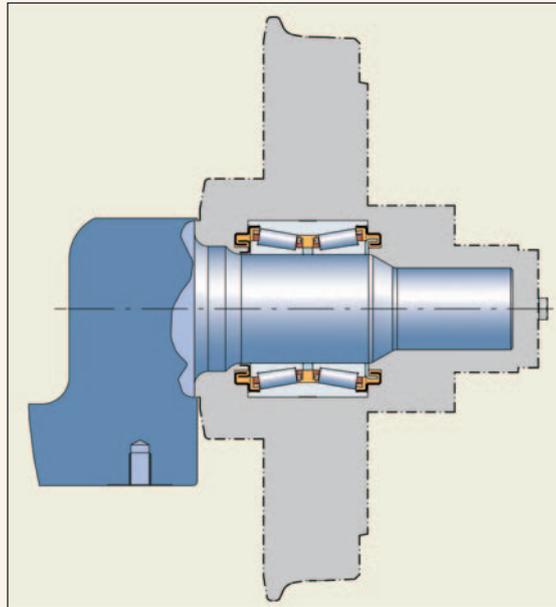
Principio del sistema de rodamiento del eje-puente.
